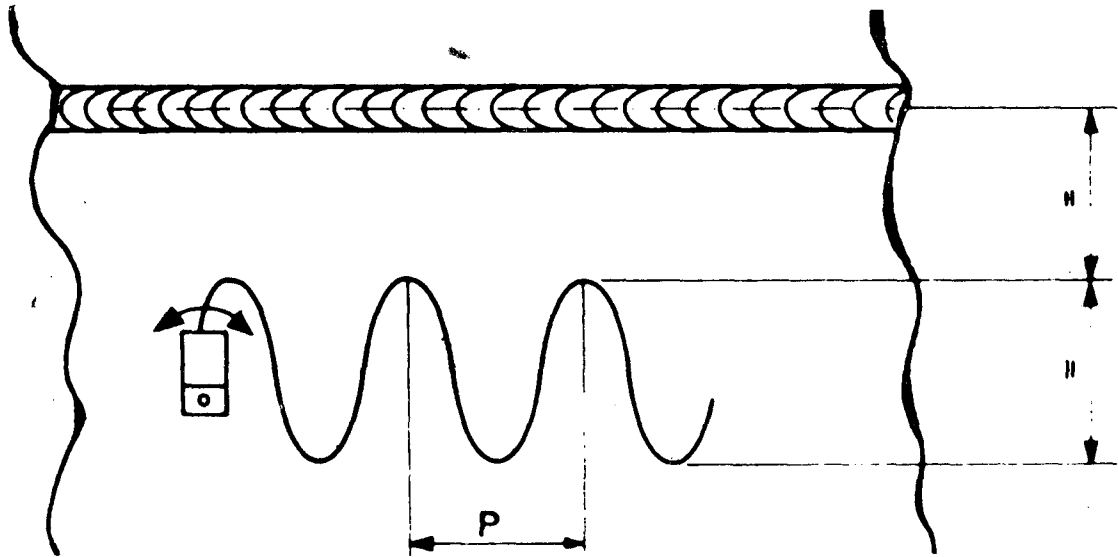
Esquematización de los movimientos fundamentales a imprimir al palpador en el examen de soldaduras.
